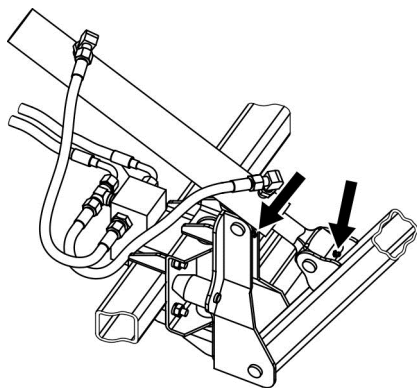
Смазка пальцев гидроцилиндра прокладчика лыжни
